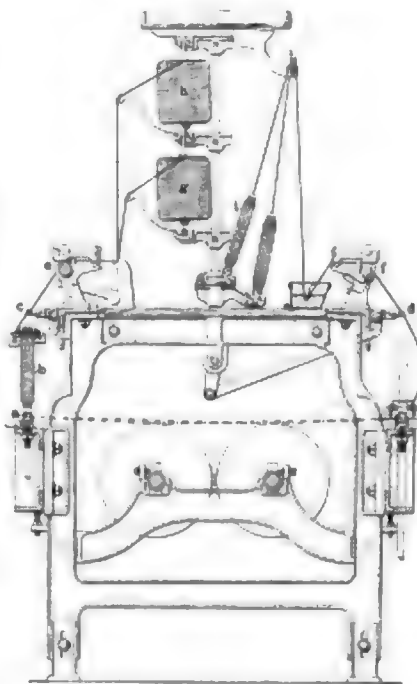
Ringzwirnmachine von der Liegnischen Maschinenbau-Gesellschaft in Muthausen i. P.
